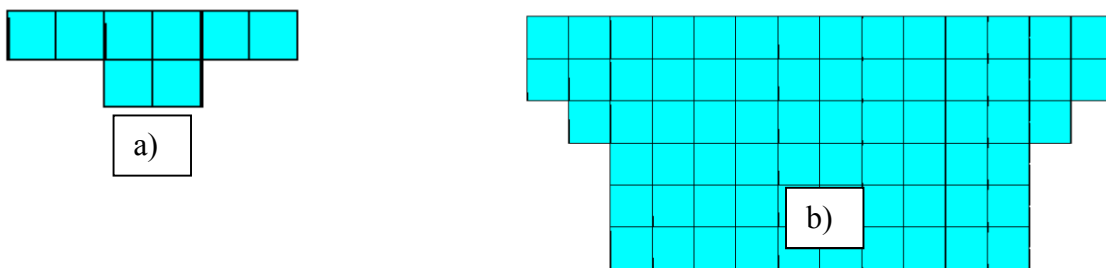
Géométrie numérique du cordon pour le jeu optimal de paramètres du plan d'expérience combiné - a) vitesse de soudage 4.3 mm/s - b) vitesse de soudage 2.6 mm/s
